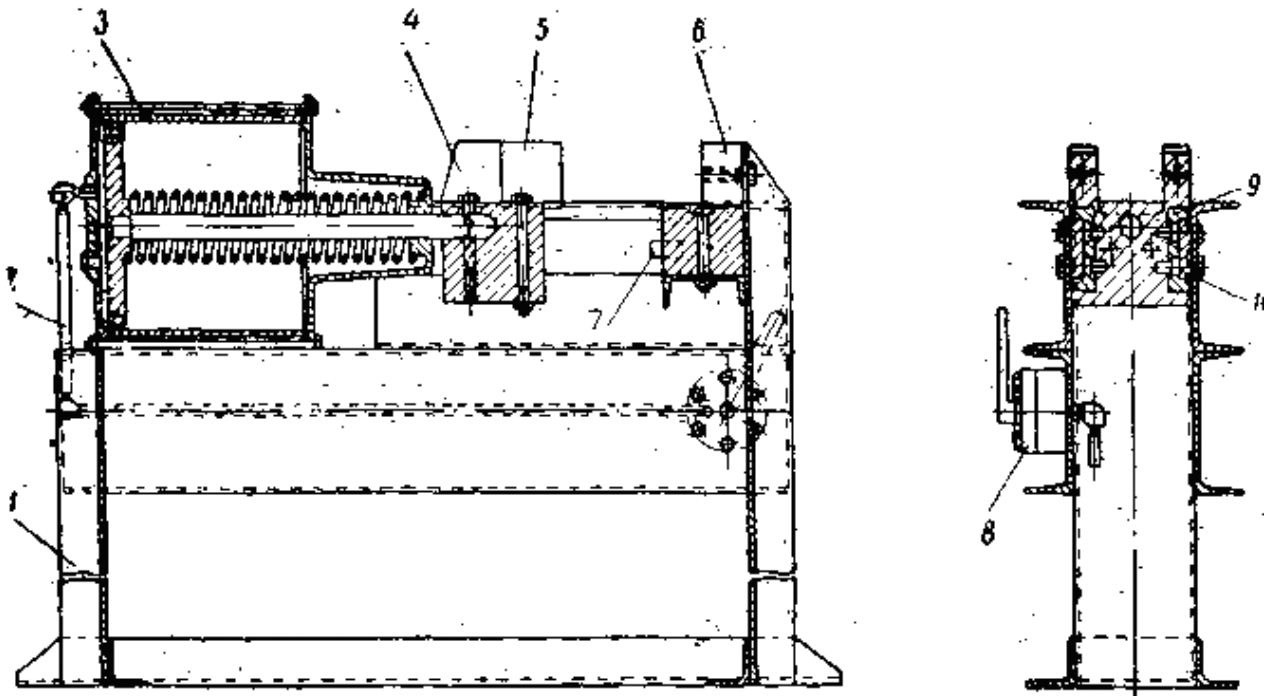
Пневматичний стенд для збирання ресор
